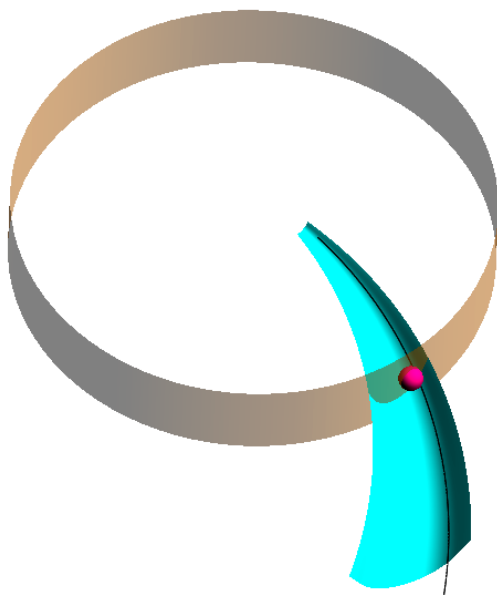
Касание сферической фрезы с поверхностью выходной детали в точке заданной линии. Показан цилиндр, на котором лежит центр фрезы
